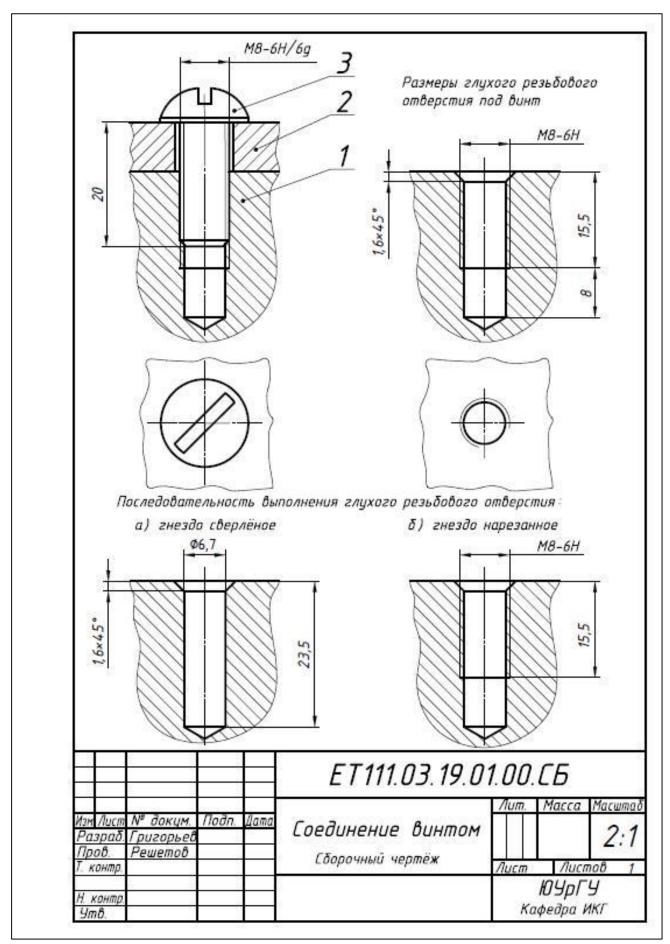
Пример выполнения сборочного чертежа винтом с полукруглой головкой
